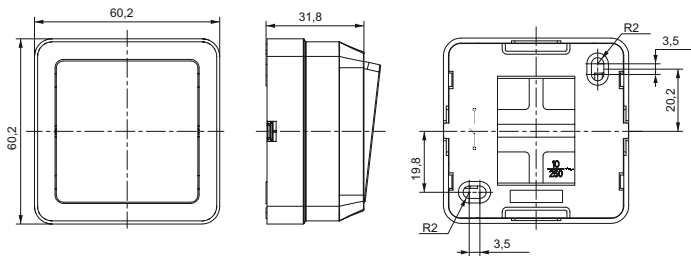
Габаритные и установочные размеры выключателя / Figure 2 – Overall and mounting dimensions of switch /
